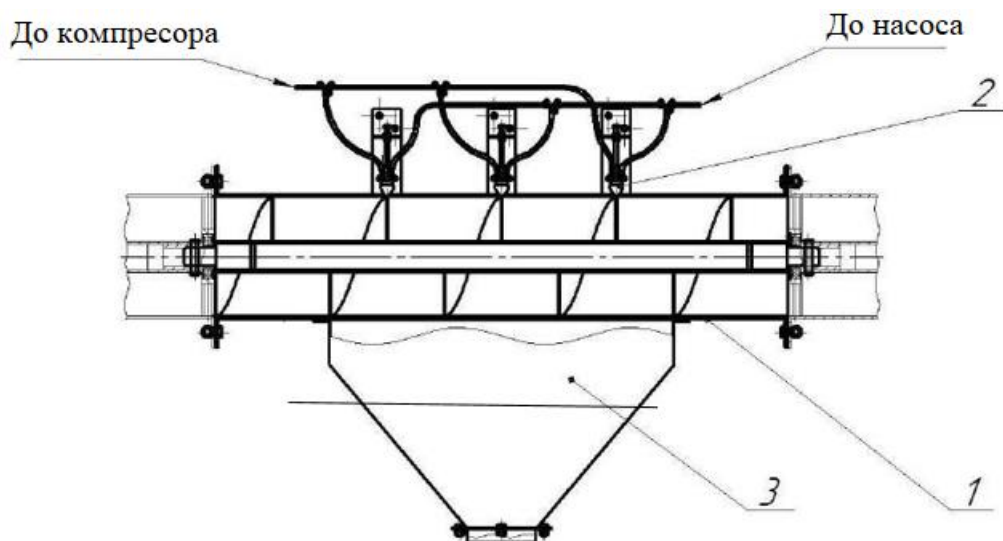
Схема камери обробки: 1 – камера обробки; 2 – розпилювач; 3 – дифузор
